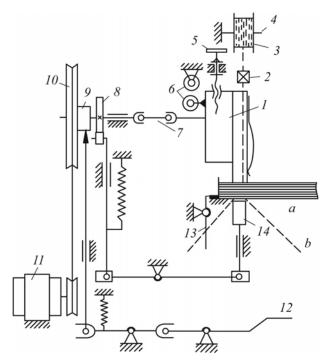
Устройство проволокошвейной машины БПШ-4:
